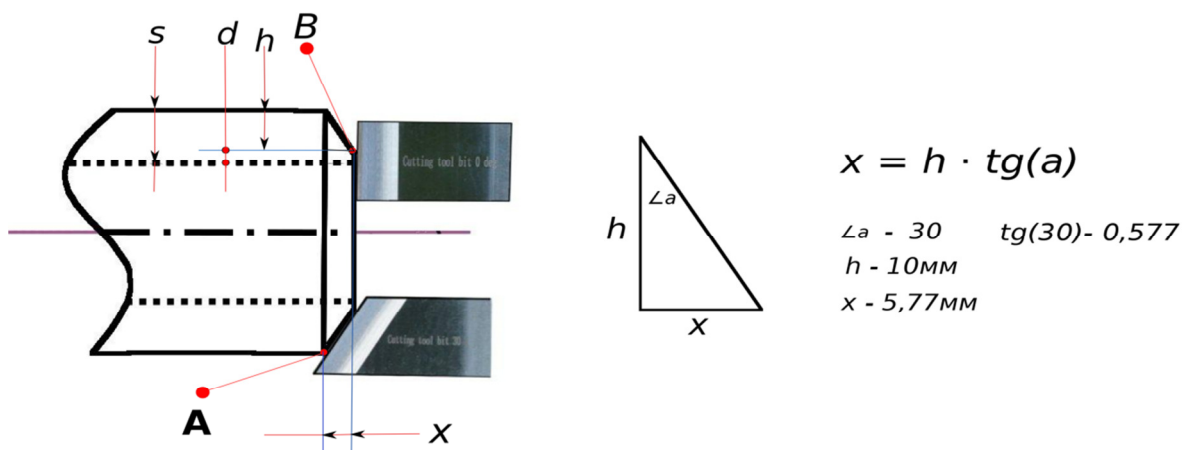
Схема положения резцов торцевателя относительно торца трубы
